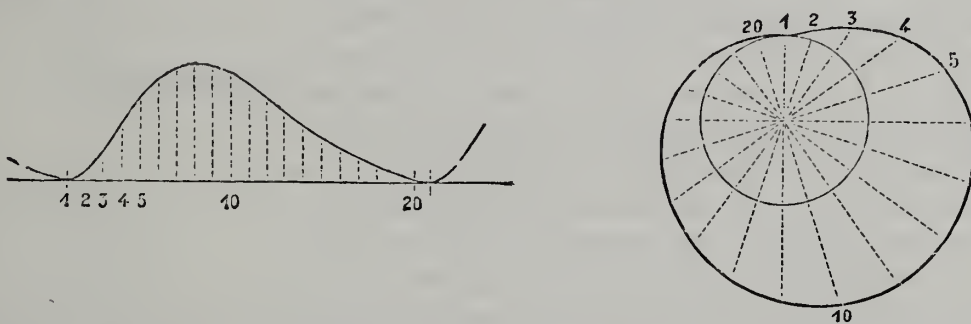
et 43. — Construction d'un excentrique destiné à imiter un mouvement quelconque.
